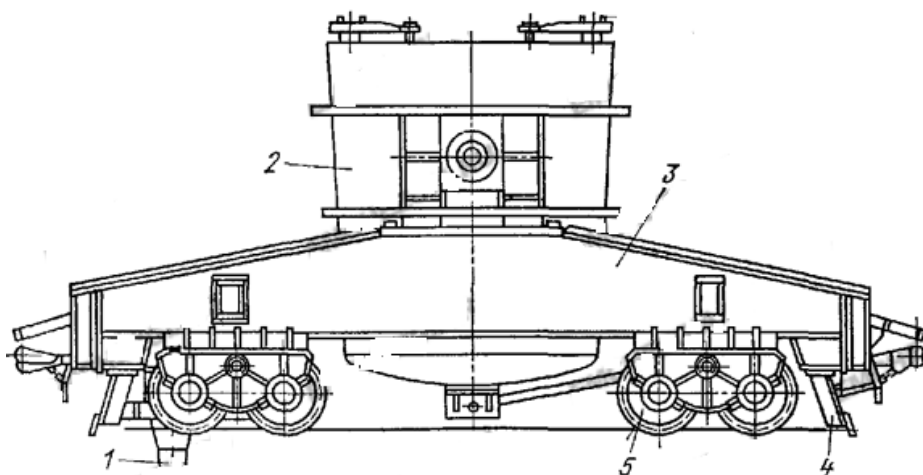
Схема сталевоза: 1 – держатель токосъемников; 2 – ковш; 3 – тележка; 4 – скребок; 5 – ходовое колесо
